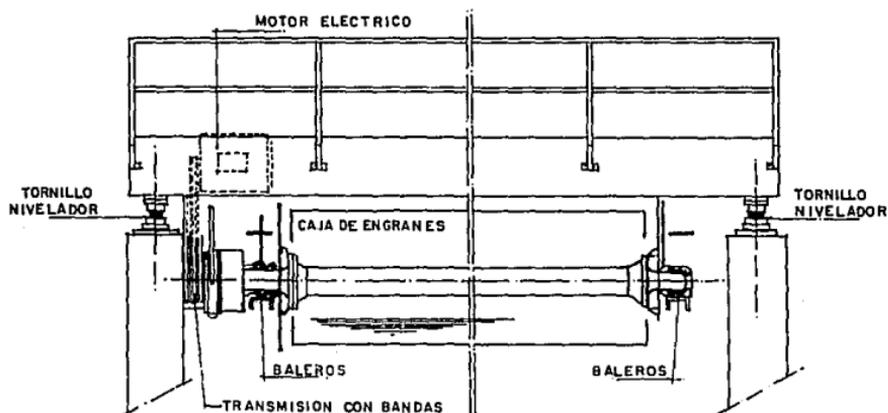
ESQUEMA DE UN ROTOR INSTALADO EN LA ZANJA.
